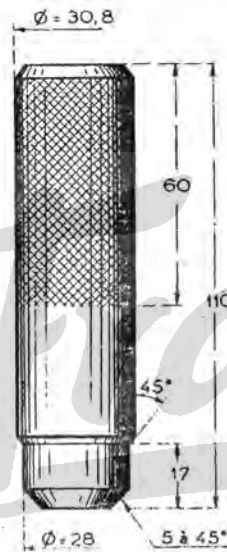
Schlüssel für Muttern der Befestigungsbolzen
